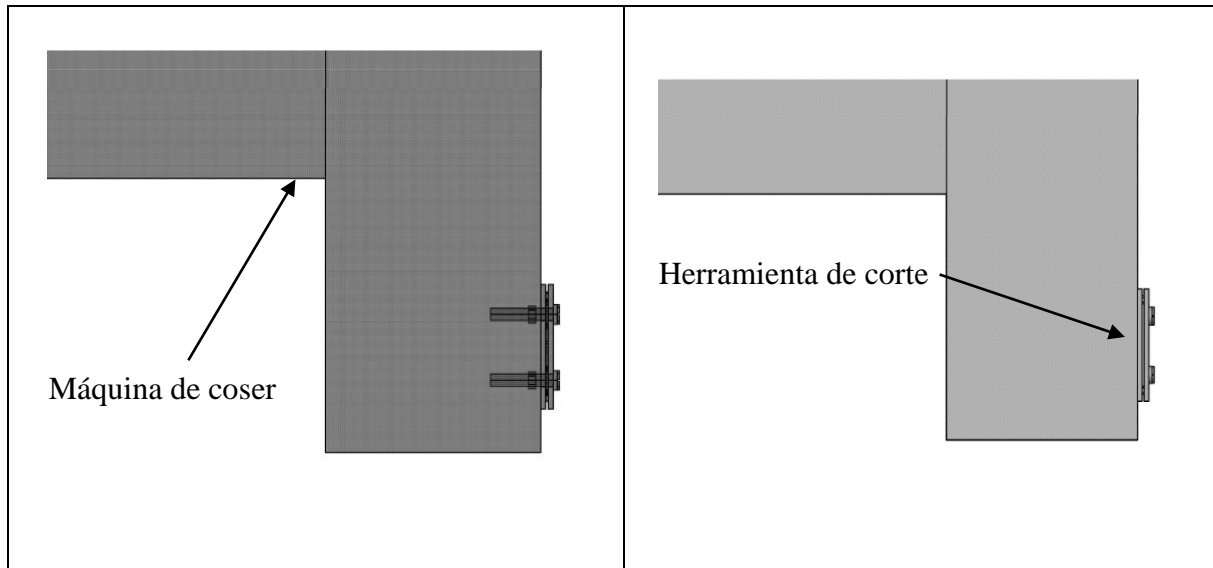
Vista lateral izquierda del dispositivo de corte ensamblado
